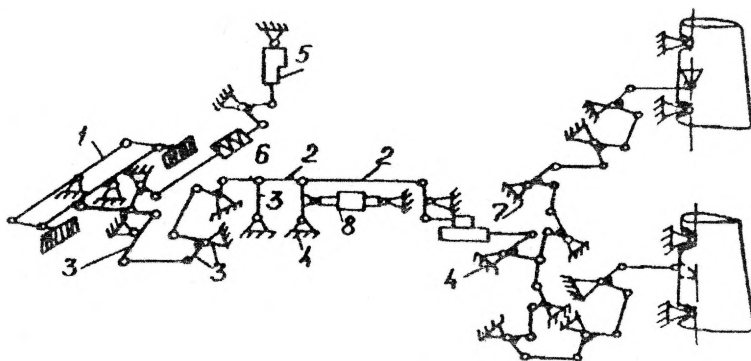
Схема канала управления рулями направления: 1 — ножной пост управления; 2 — тяга; 3 — качалка; 4 — кронштейн; 5 — механизм триммерного эффекта; 6 — загрузочный механизм; 7 — бустер; 8 — рулевая машина автопилота
